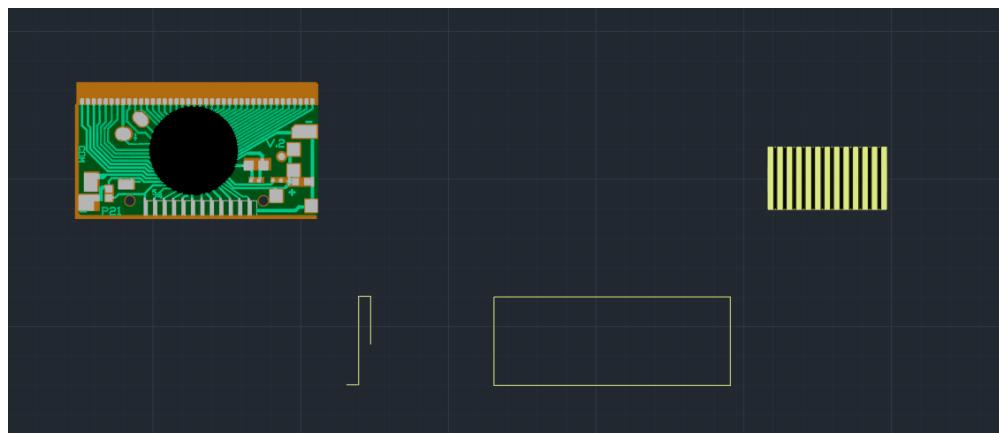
PCB-ul și cele două benzi cu care este prins de ecran fără cotare
